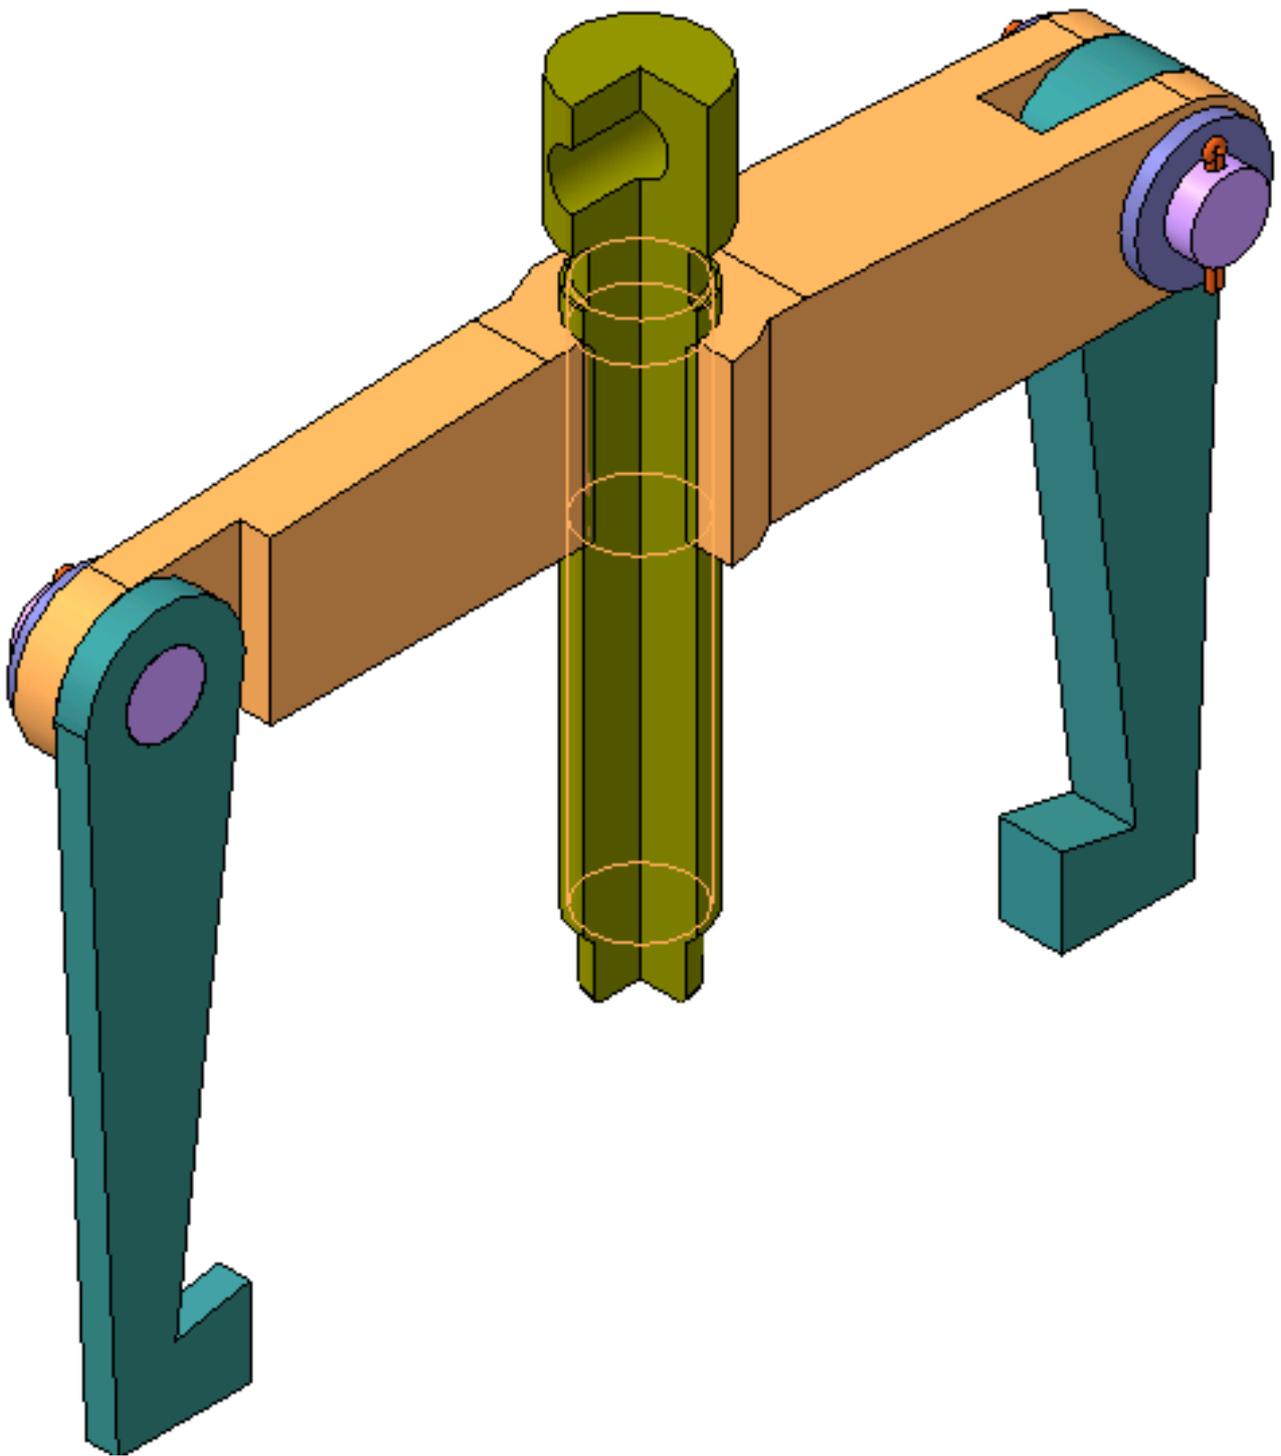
3D-модель сборки изделия «Съемник-2» (варианты 17, 37)
